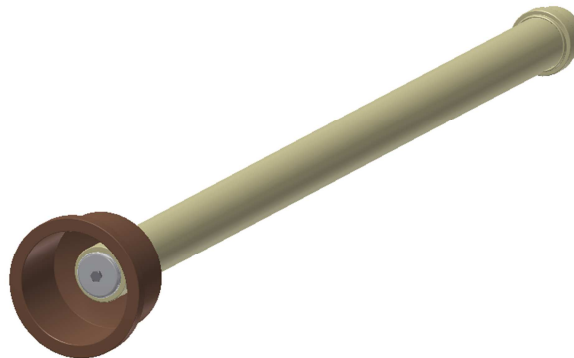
Tubo do conjunto divisor capacitivo e tampa do abrigo
